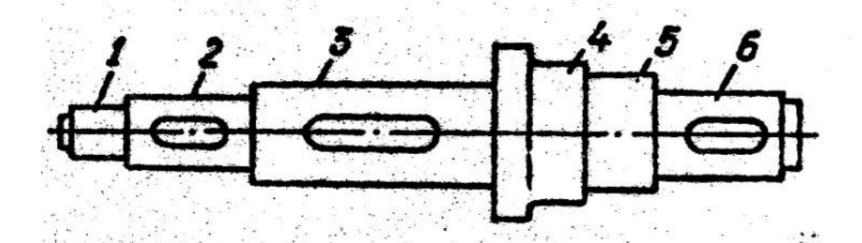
Вал машины постоянного тока с указанием мест закрепления основных деталей якоря: I и 5 - для подшипников; 2 для коллектора; 3 - для сердечника якоря; 4 - для вентилятора; 6 - свободный конец вала
